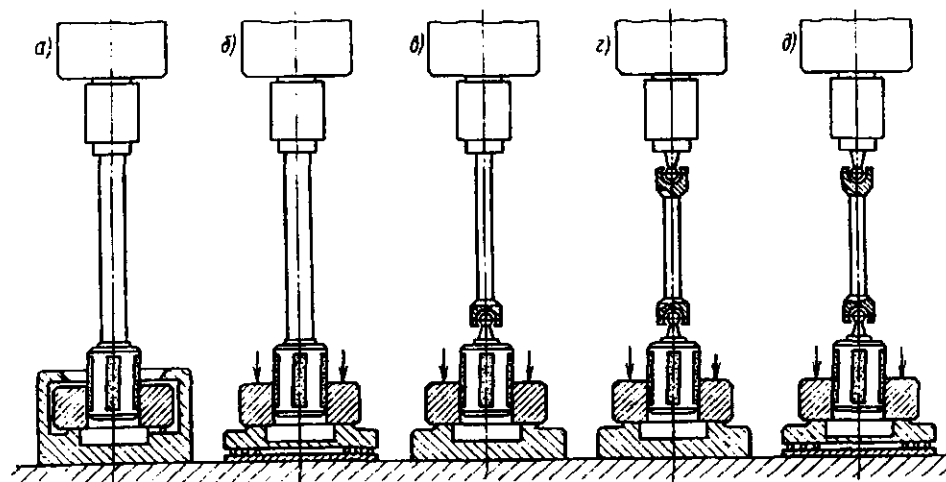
Схемы установки и крепления детали и инструмента при хонинговании
